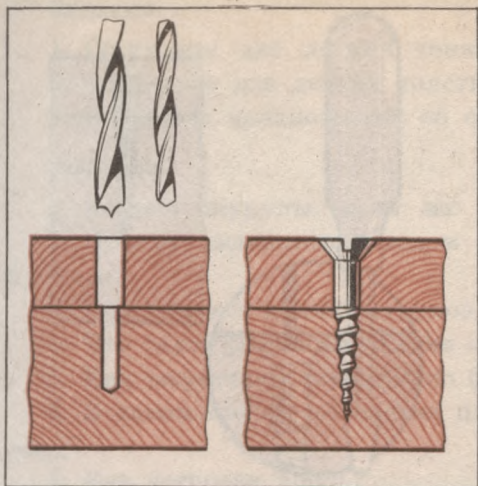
Сверление отверстия под шуруп двумя сверлами.
